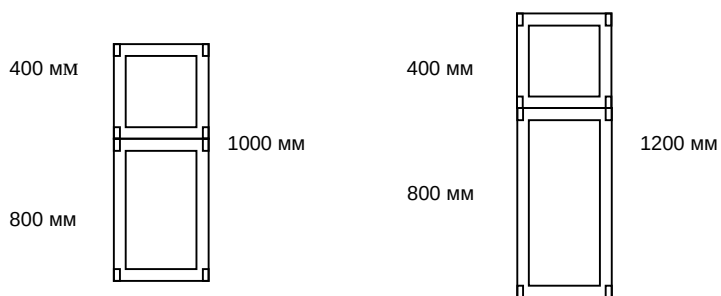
Варианты сборного каркаса для шкафа (вид сверху).
